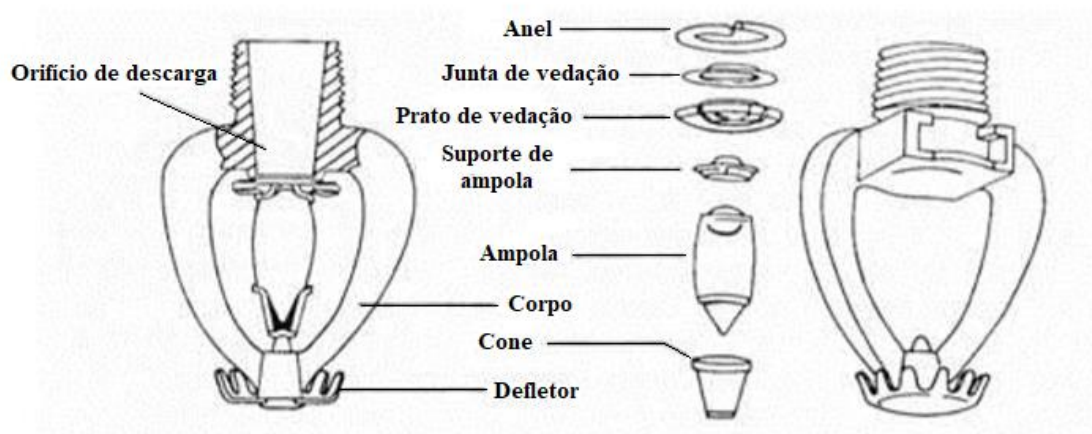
Constituição de um *sprinkler* (adaptado da Nota Técnica n.º 16, 2011)
